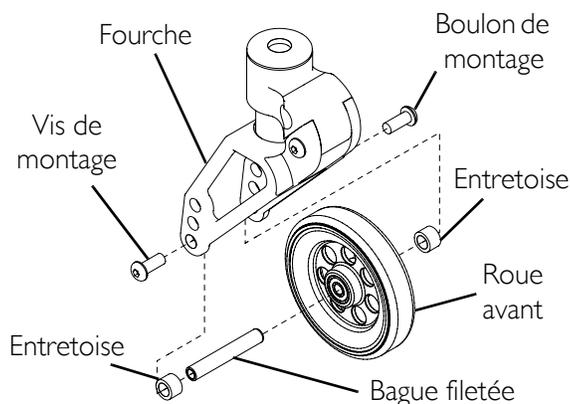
Enlever/Installer/Repositionner l'assemblage de la roue avant - Fourches à suspensions
